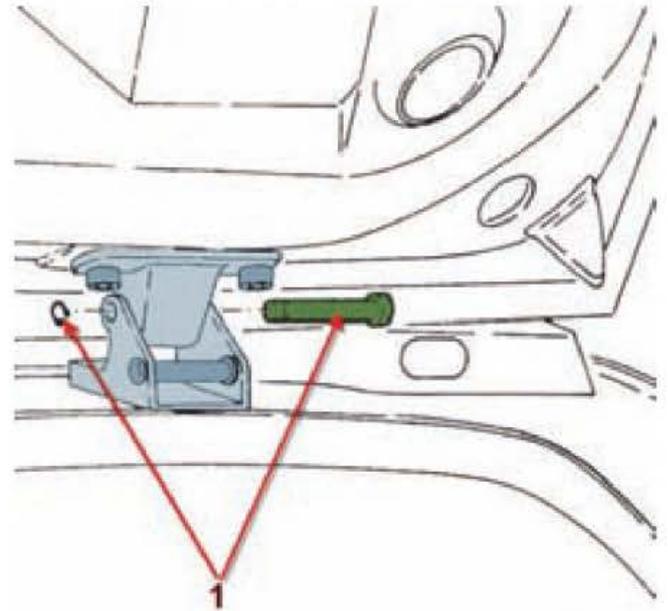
Desmontaje del pasador de las bisagras soldadas del portón.
